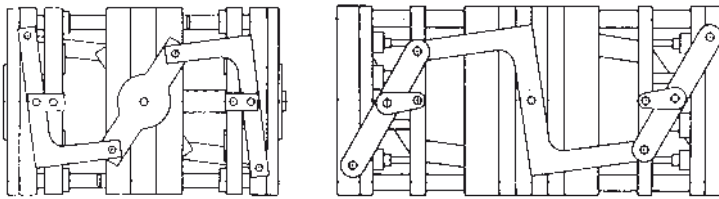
Bewegung des Werkzeugmittelsegments und der Auswerfer mit Hilfe von Gelenkhebel [13.12]
